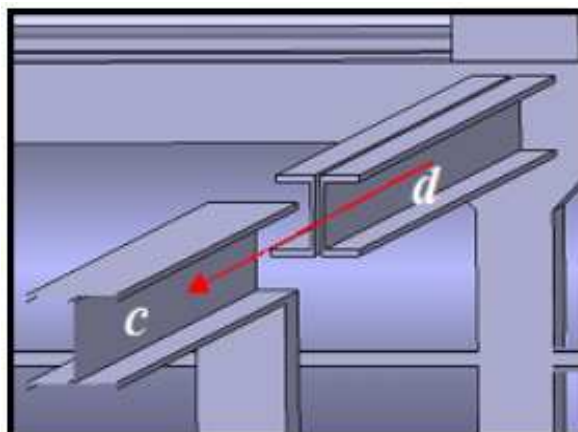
14: Acoplamiento travesaño superior. “c” indica estructura fija. “d” indica estructura móvil.
